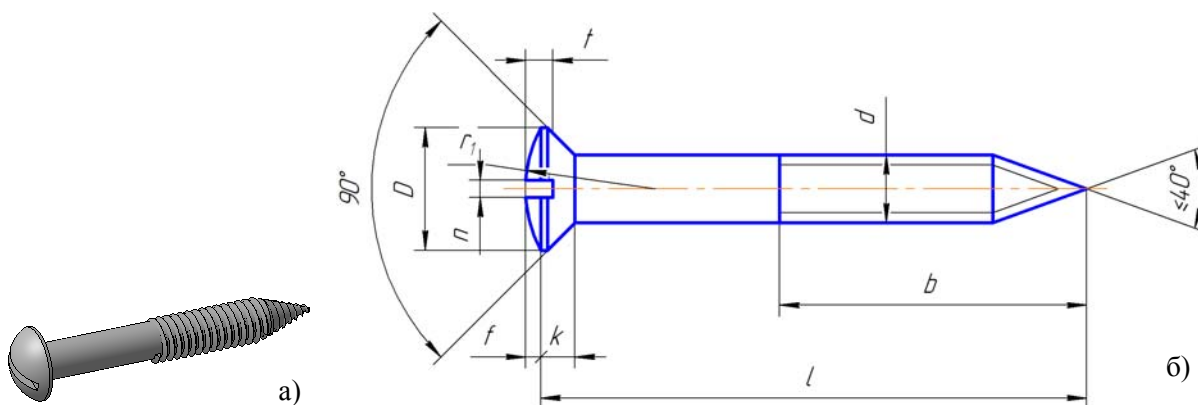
Шуруп: а – внешний вид; б – чертеж
